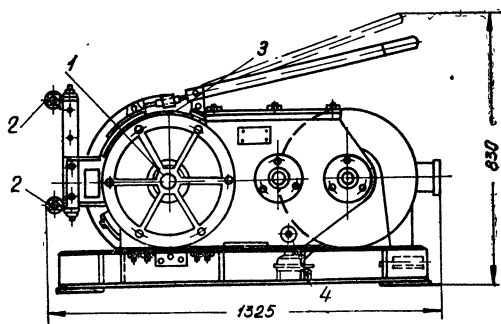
Смазка скреперной лебедки ЛУ-16:
